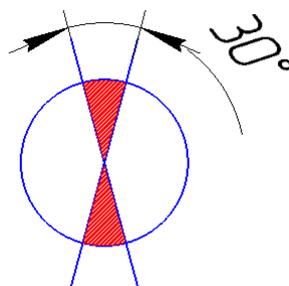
Схема с указанием зон начала-окончания сварки
